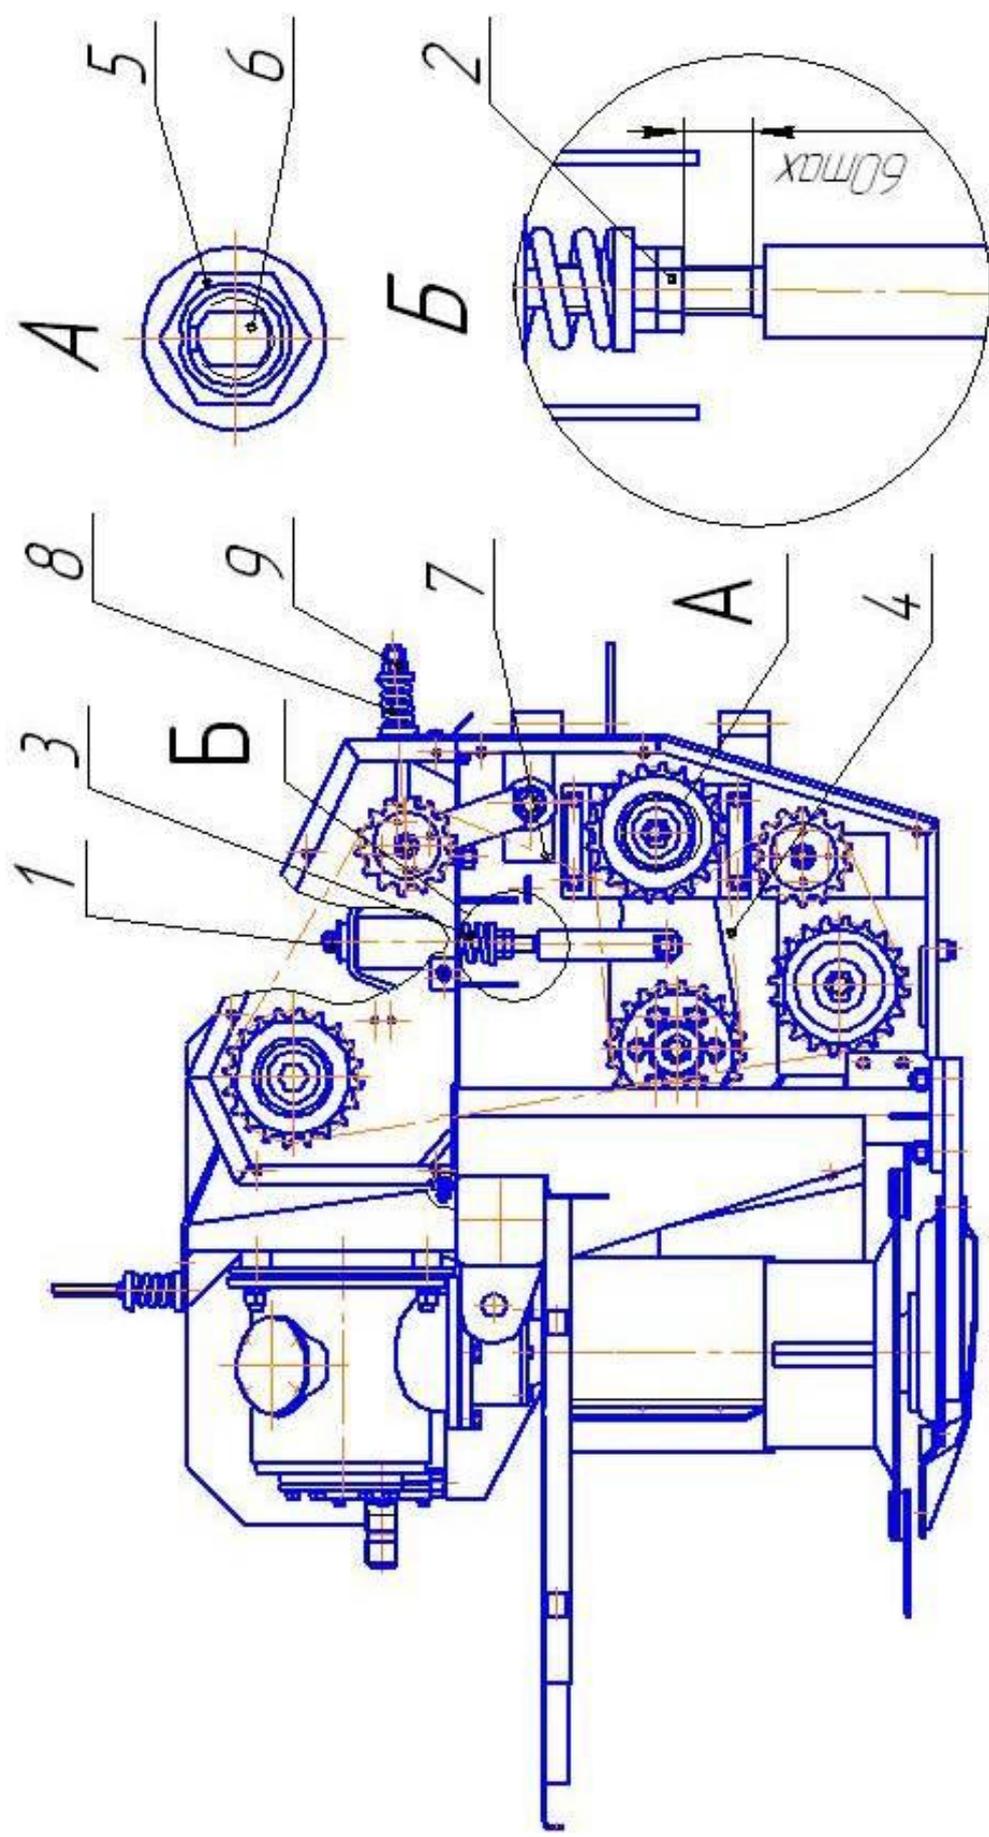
Регулировка зазора между вальцами и цепной привод косилки КДП-310
